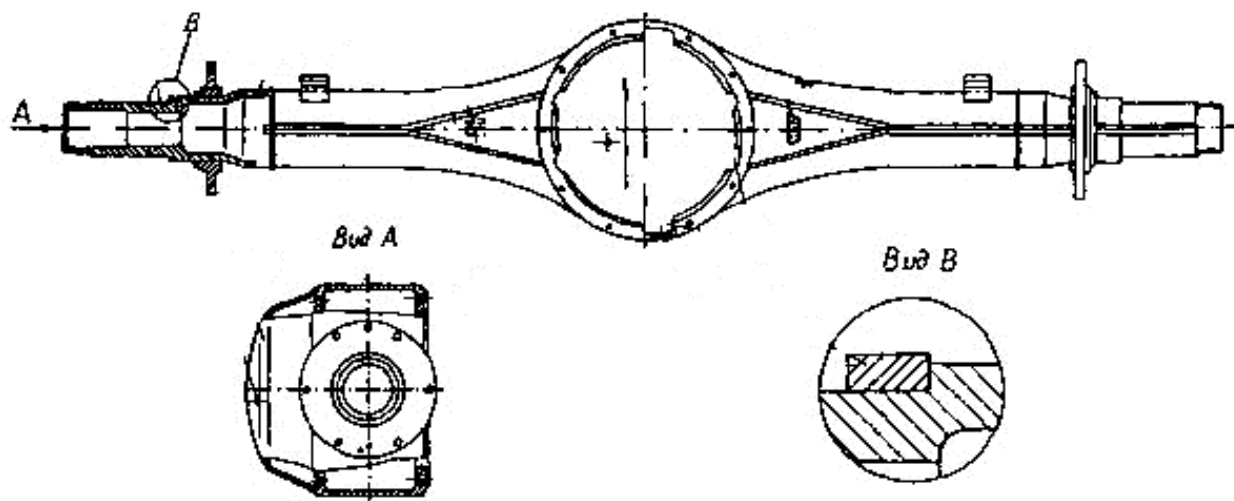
Конструкция штампованно-сварной балки типа «банджо»
